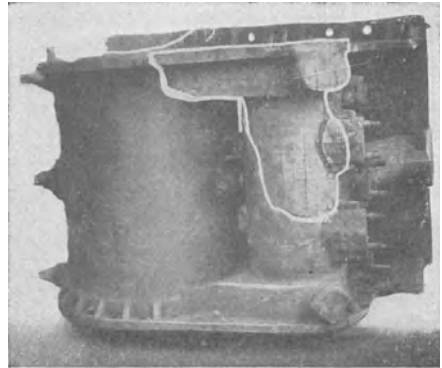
Lokomotivzylinder (Abb. 328) nach der Schweißung.
